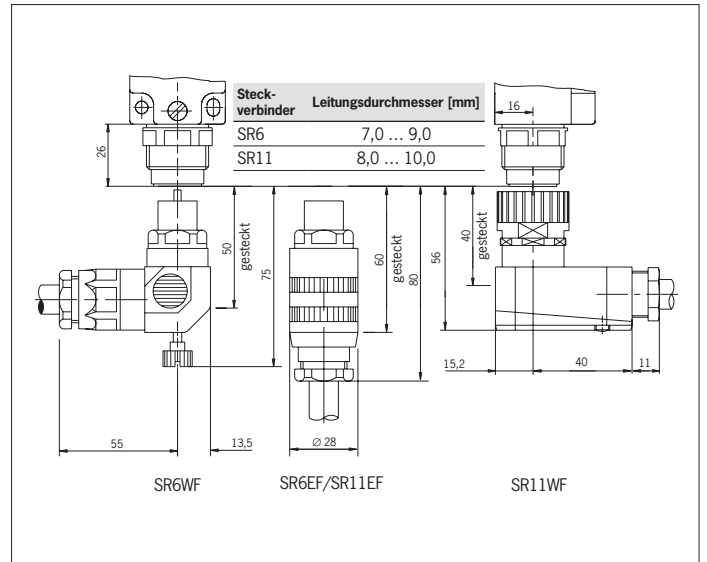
Maßzeichnung NZ2... mit Steckverbinder
